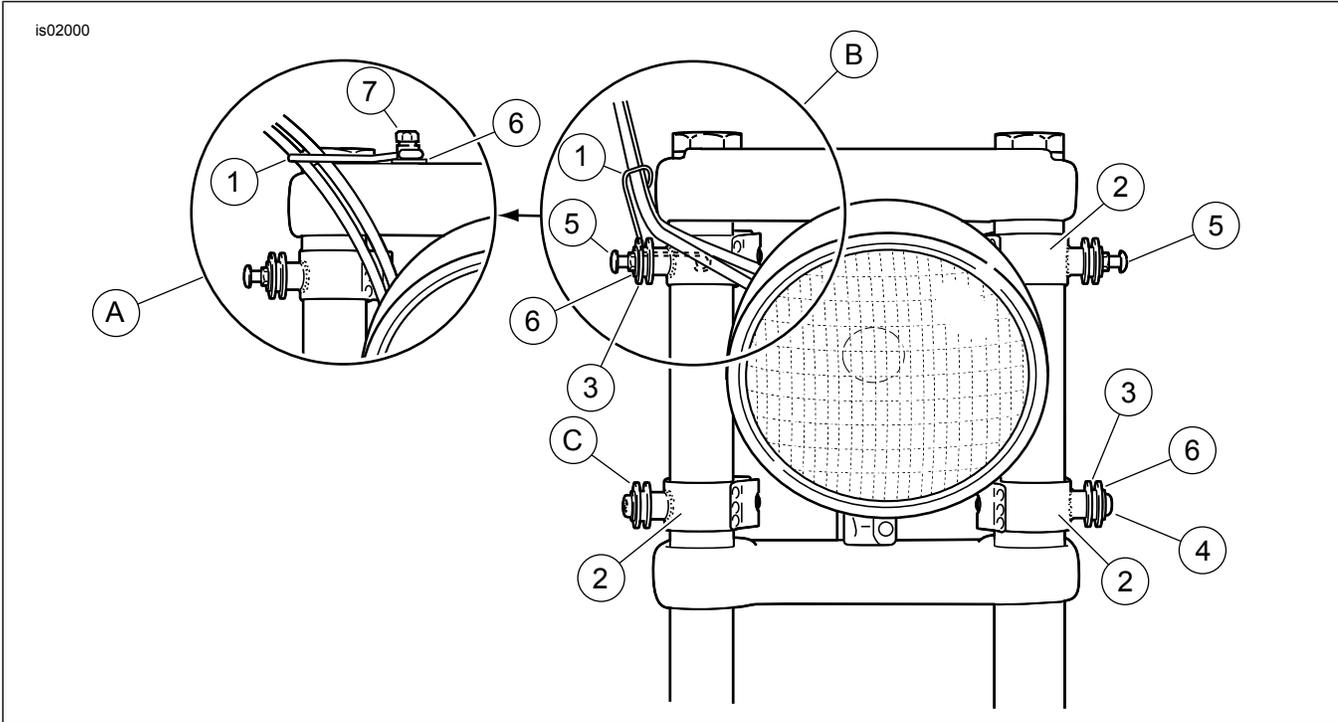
Service Parts 5: Abschließbare Windschutzscheiben-Befestigungsteilesatz
